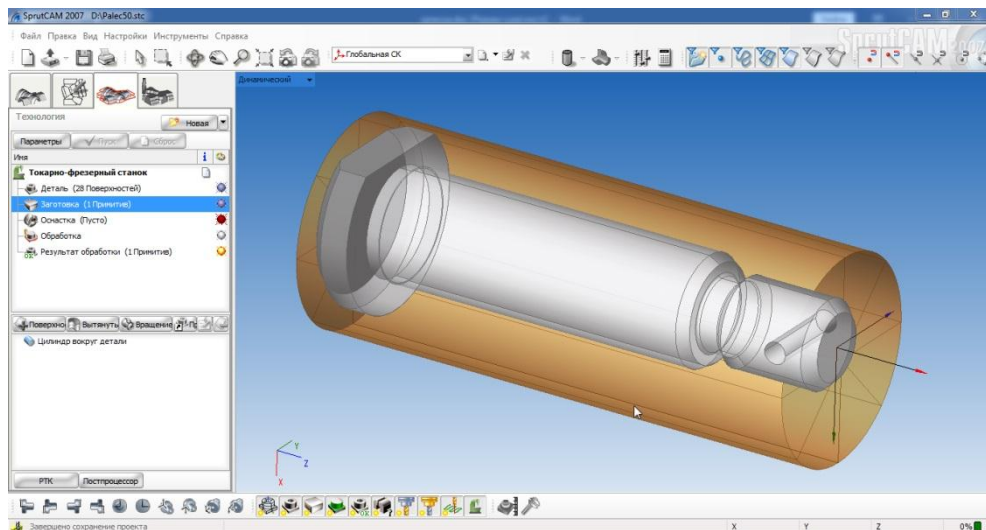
Деталь та заготовка в системі СПРУТ-САМ
